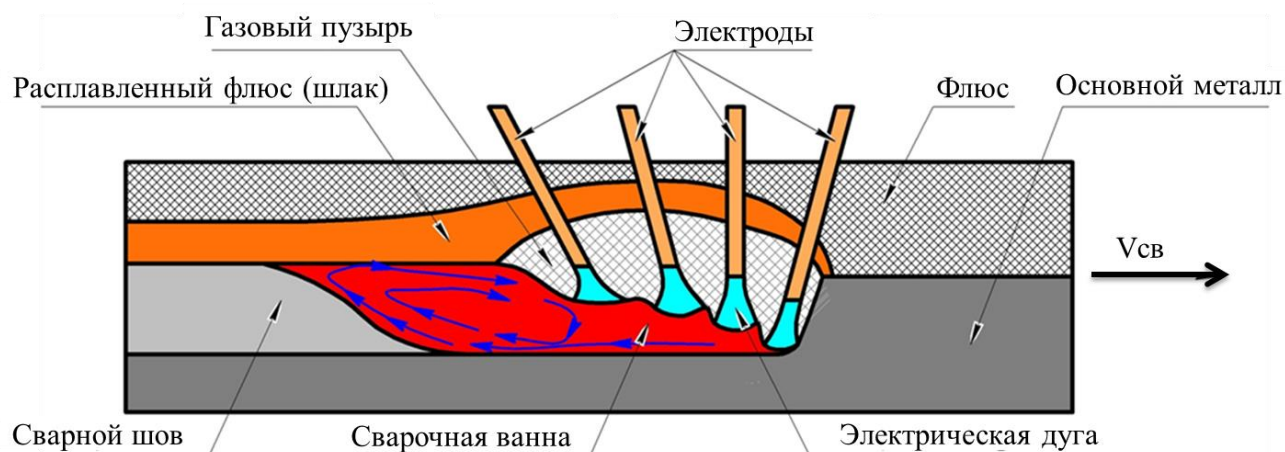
Схематическое изображение автоматической многодуговой сварки под флюсом
